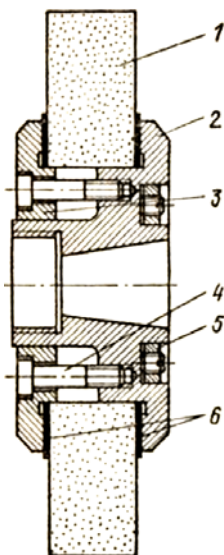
Крепление шлифовального круга на планшайбе:
